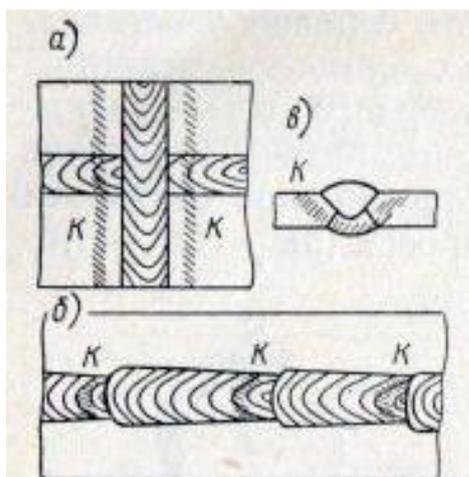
Межкристаллитная коррозия в результате выпадения карбидов а - при сварке пересекающихся швов; б - при возобновлении сварки шва после смены электрода; в - при двустороннем сварном шве
